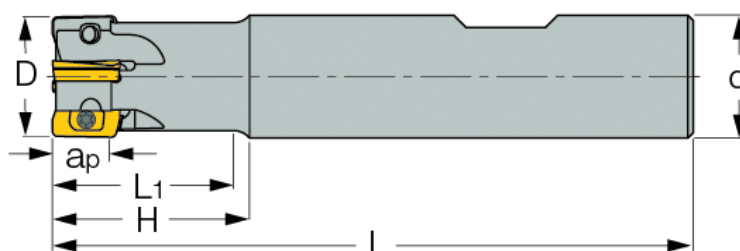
Корпус фрезы HP E90AN-D16-3-C16-07-C
